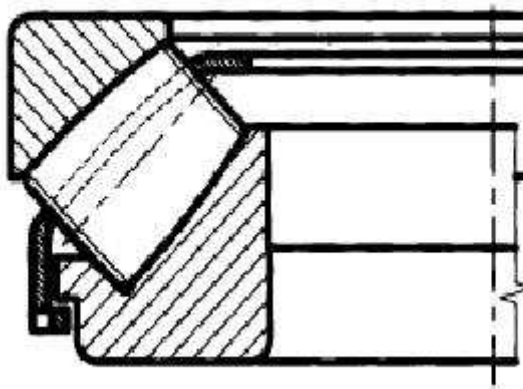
Axiální soudečkové ložisko s masivní mosaznou klecí
